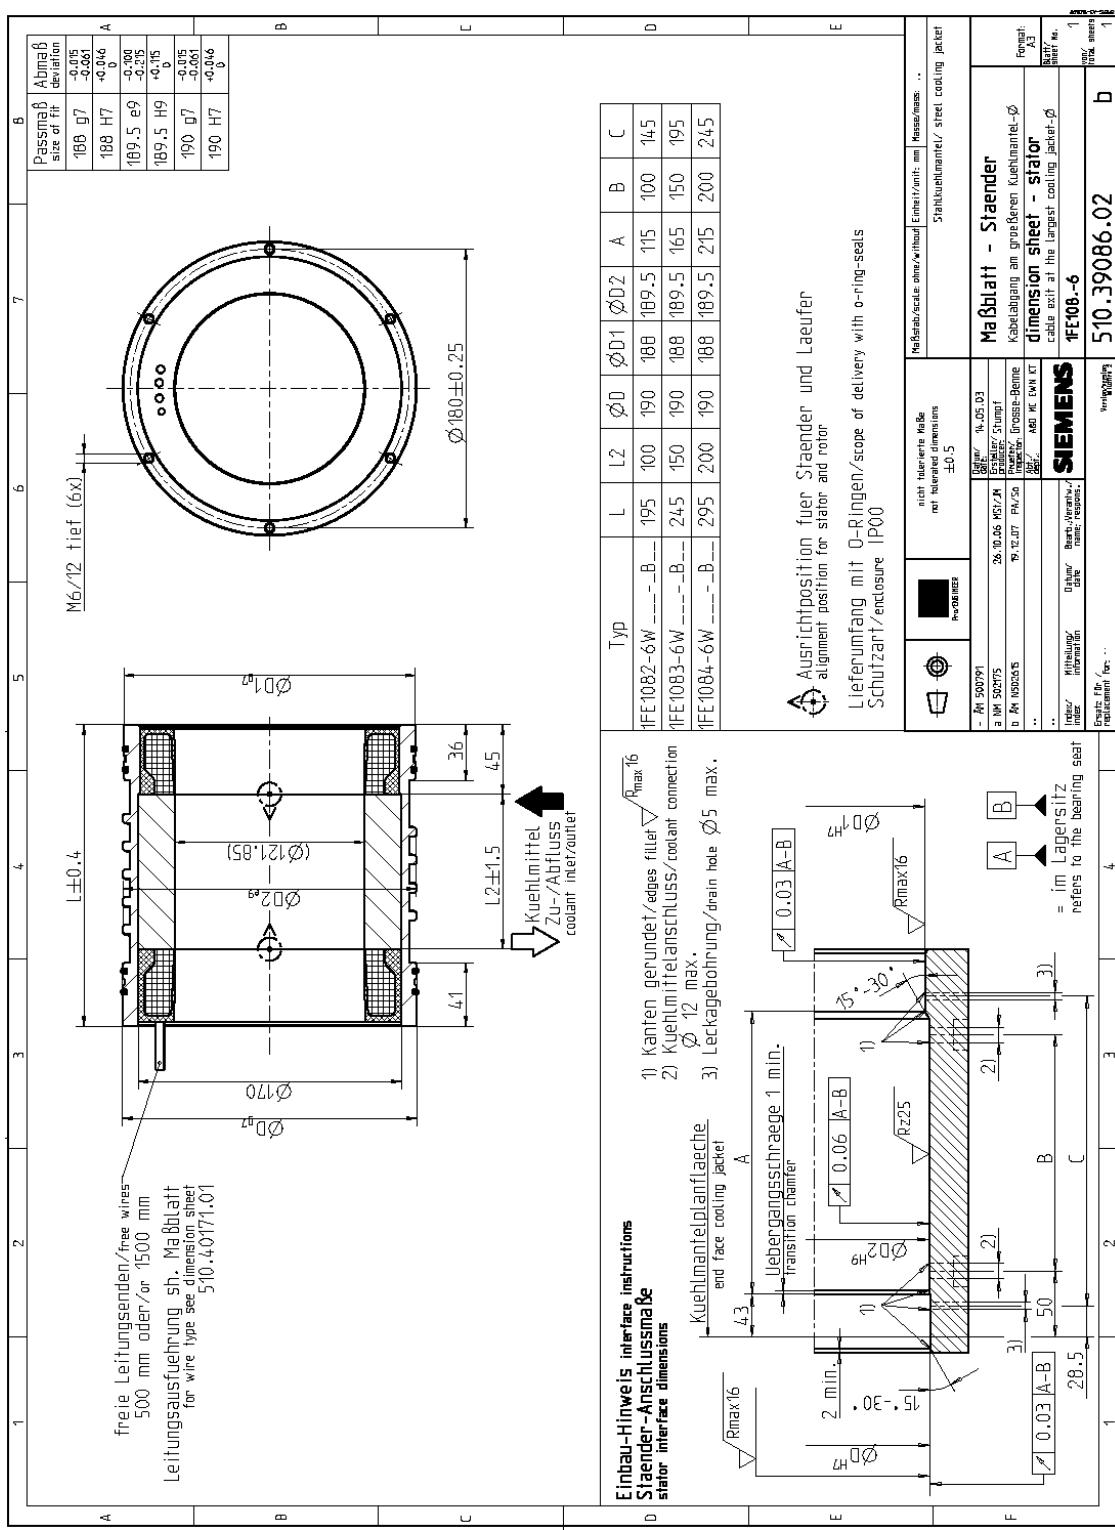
1FE108□-6, Ständer mit Kühlmantel, Kabelabgang am größeren Kühlmanteldurchmesser
